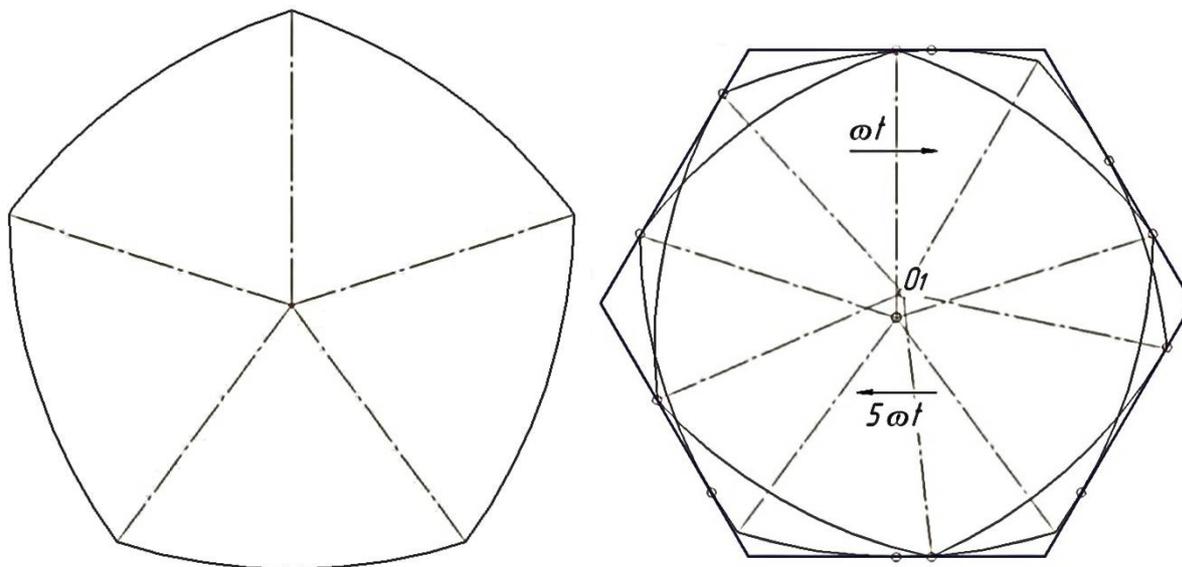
Пятивершинный РК-профиль и его обкатывание в шестиугольной направляющей рамке
